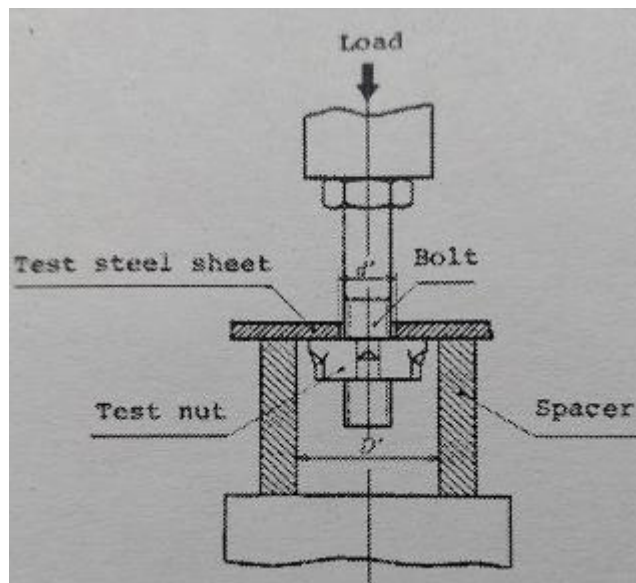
Muestra esquemática de ensayo por tracción de una tuerca soldada por proyección.
